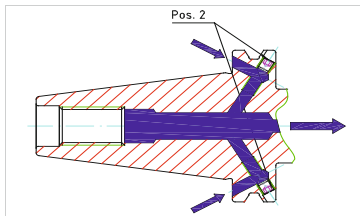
Kühlmittelzuführung Form AF/JF
